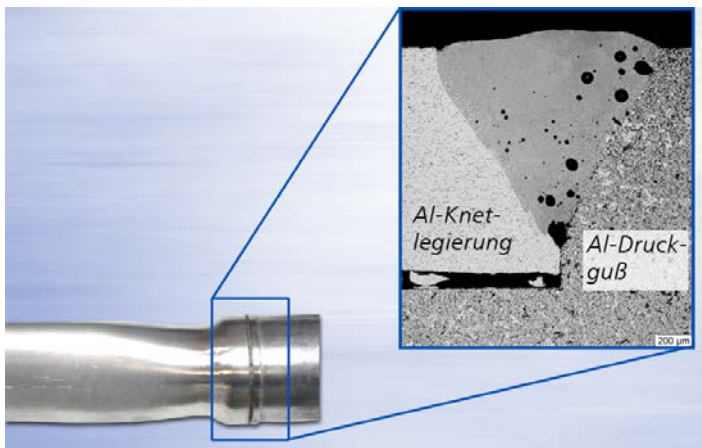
Ausschnitt aus einem Kundenbauteil mit druckdichter Schweißnaht;
